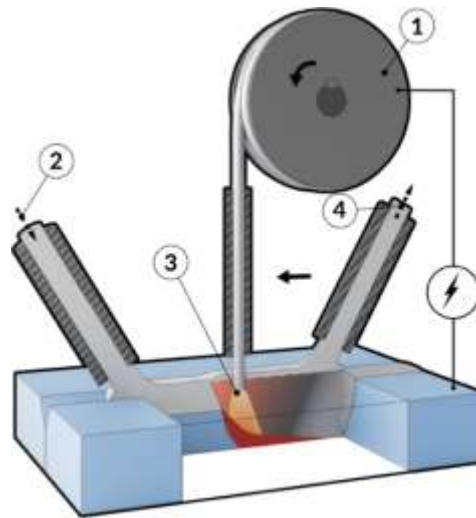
Схема автоматичного зварювання під флюсом
